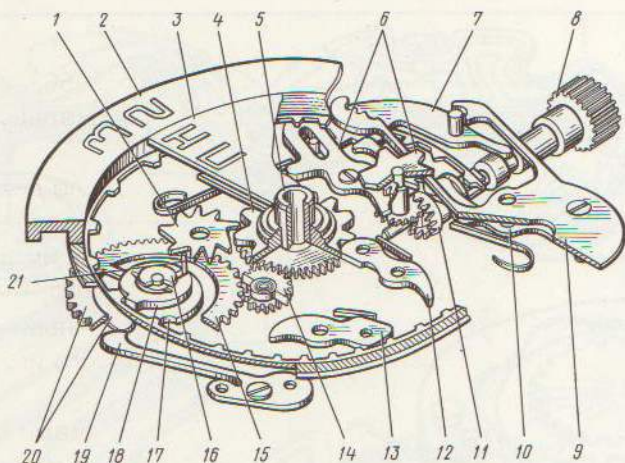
Кинематическая схема календарного устройства механизма часов 3050:
